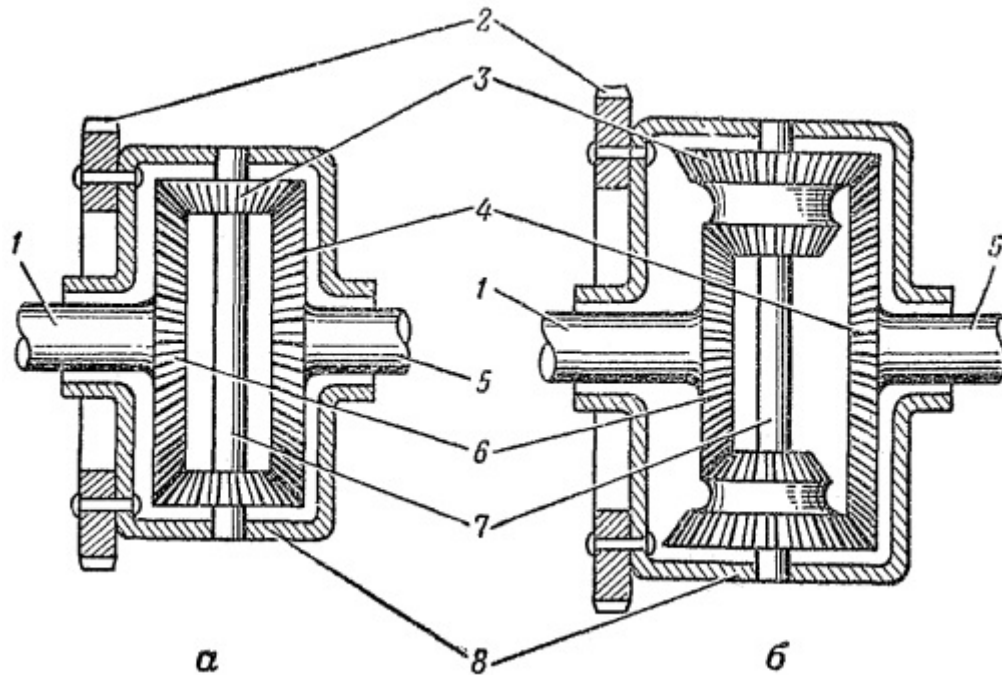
Схема межосевого дифференциала: а — симметричный дифференциал; б — несимметричный дифференциалу; 1 — вал привода переднего ведущего моста; 2 — ведомая шестерня дифференциала; 3 — сателлит; 4 и 6 — шестерни валов привода ведущих мостов; 5 — вал привода среднего и заднего ведущих мостов; 7 — крестовина; 8 — коробка дифференциала
